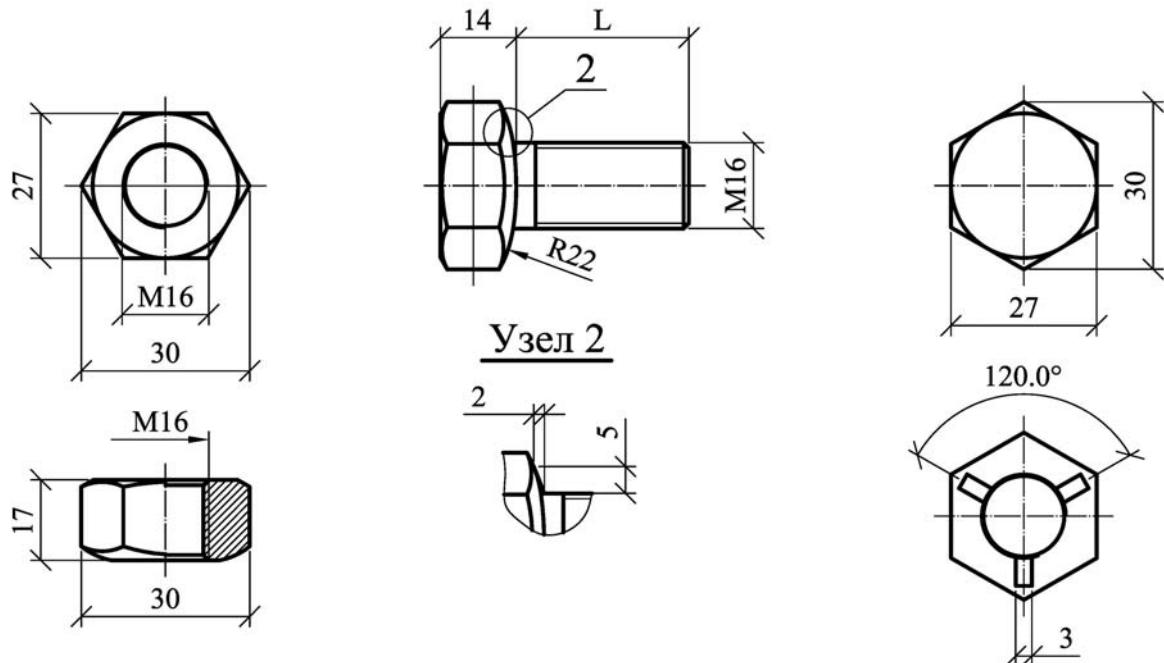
Болты и гайки для изделий ГЛ34
